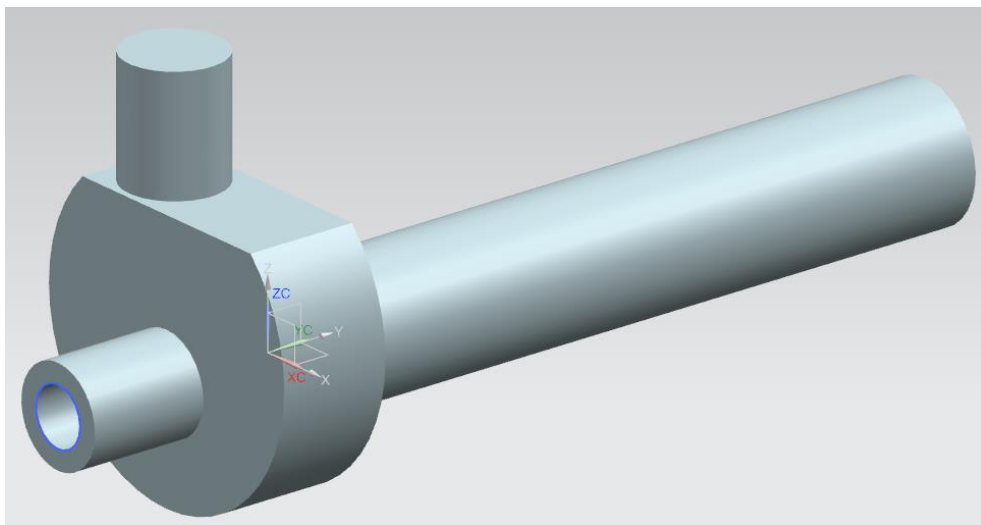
Внешний вид детали после создания канала выхода
